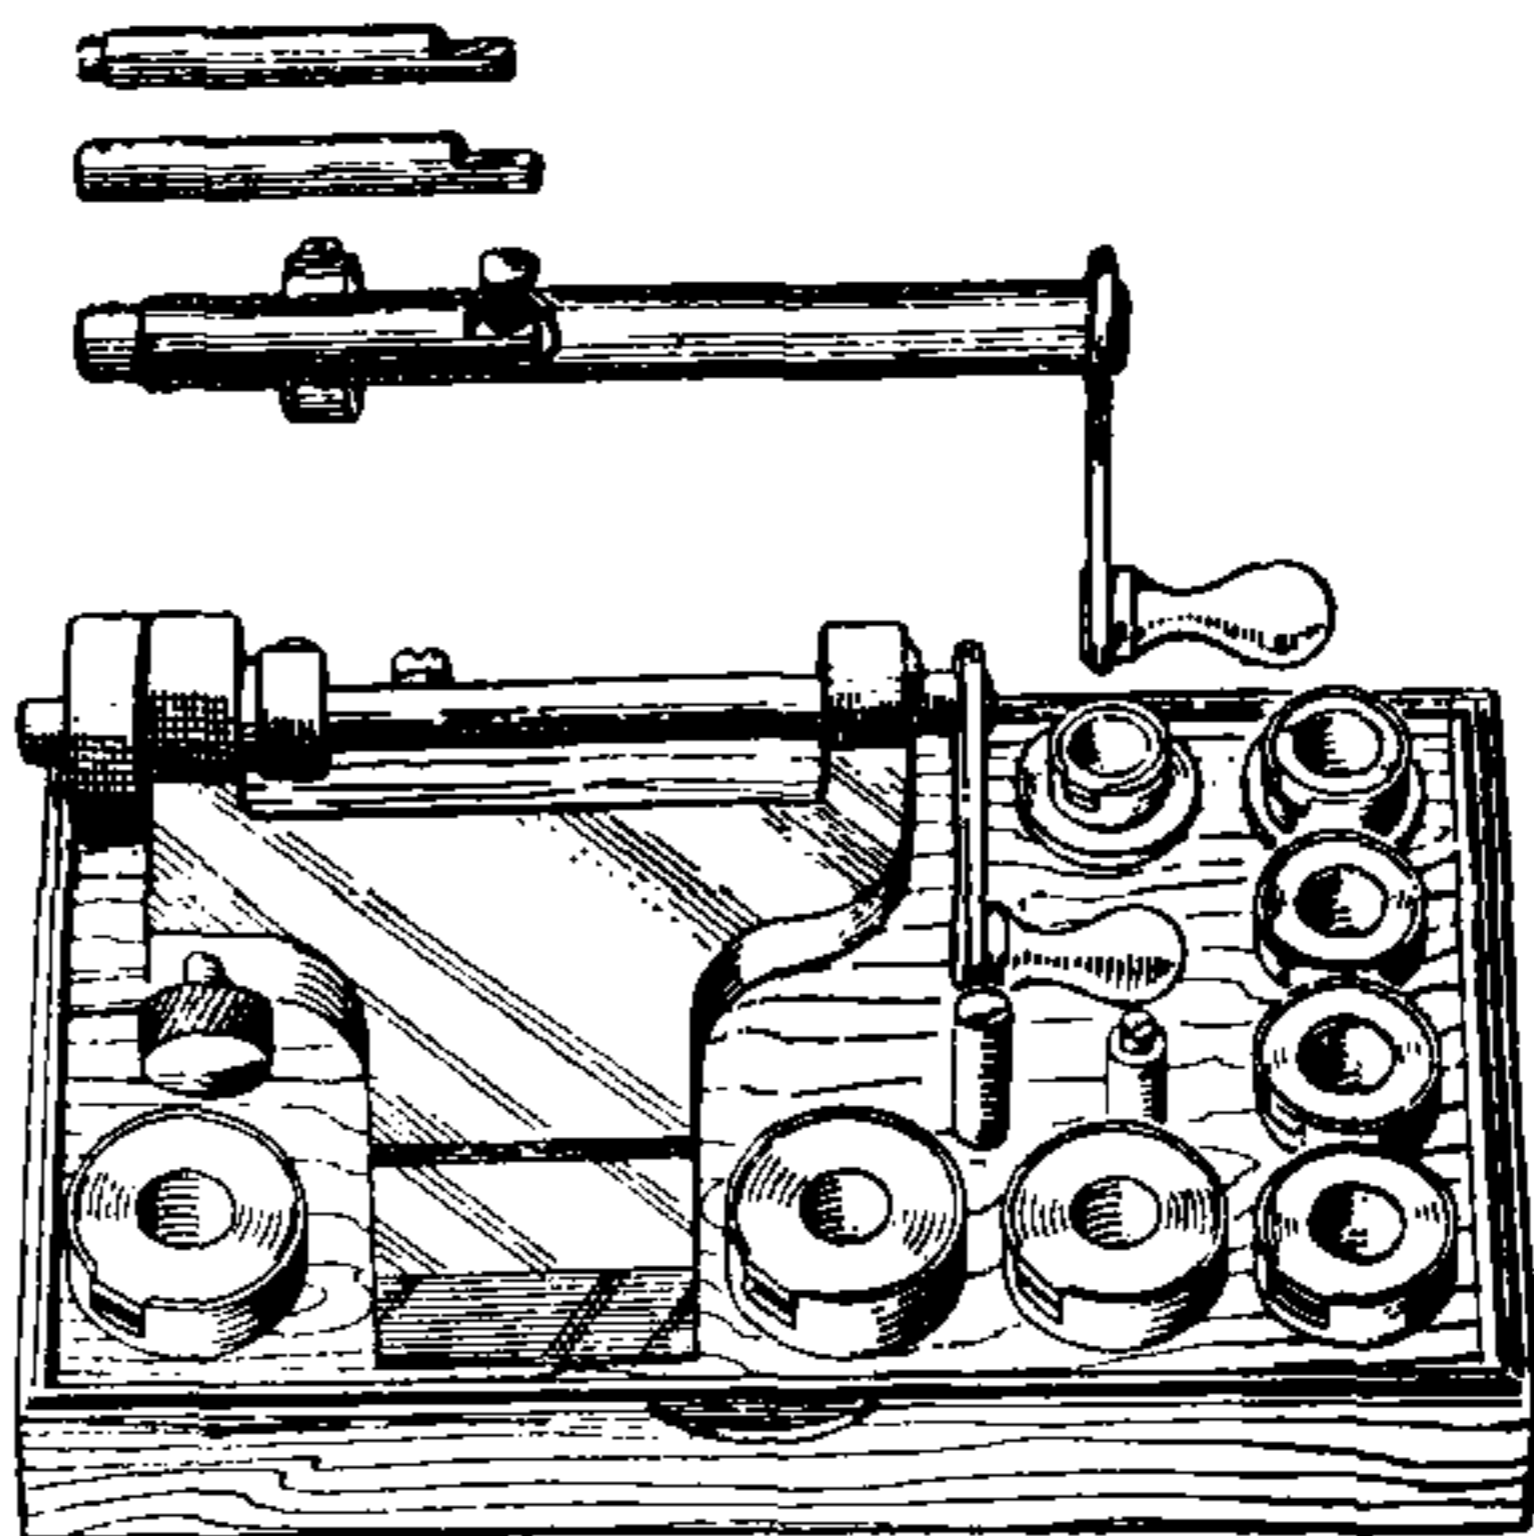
Apparecchio americano per l'avvolgimento della molla motrice nel bariletto.
